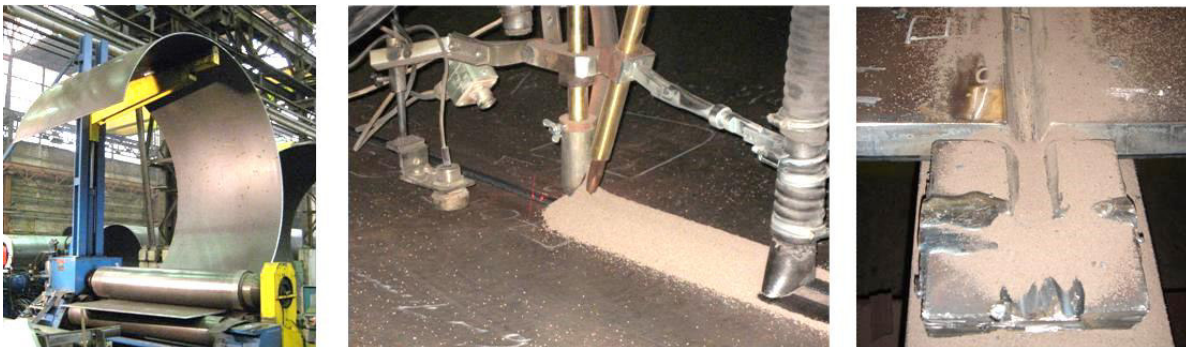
Herstellung von Stahlrohrtürmen mit Mehrdraht-UP-Schweißtechnik im Werk SIAG Tube & Tower, Leipzig; links: Walz-Biege-Vorgang zum Formen der Grobbleche; Mitte: UP-Schweißvorgang; rechts: Ein- und Auslaufblech für den UP-Prozess
